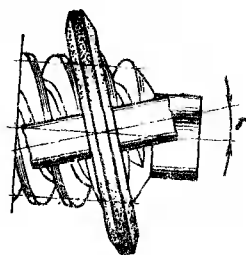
Цилиндрический, образованный конусом червяк ZK1
